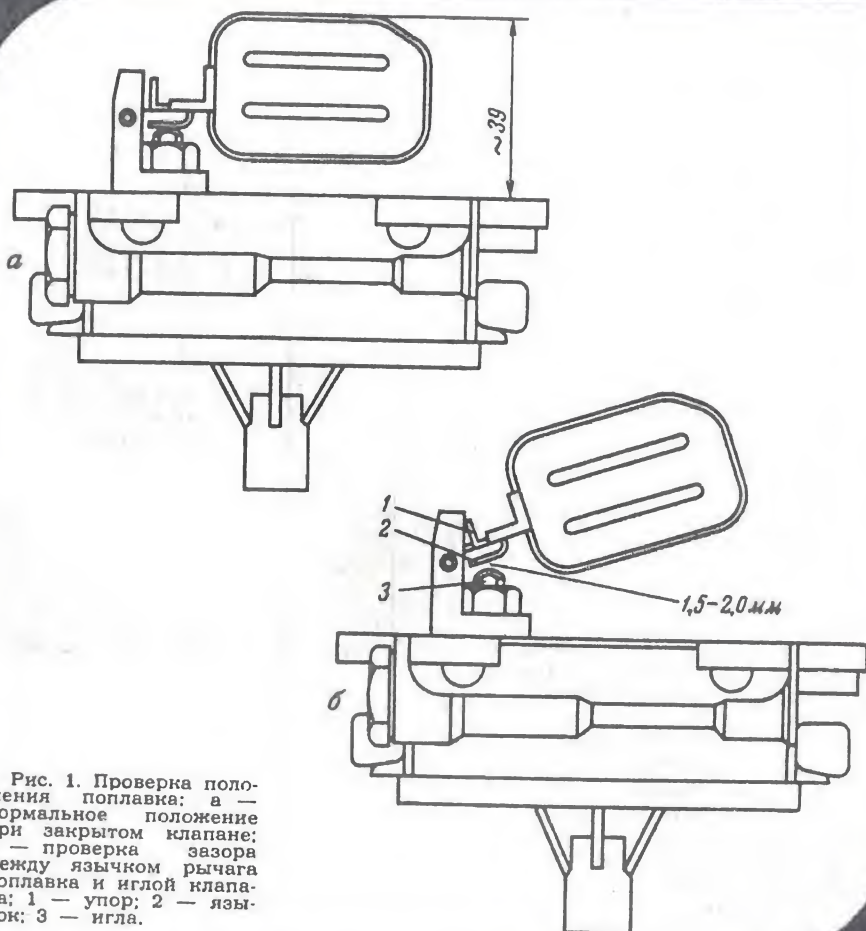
Проверка положения поплавка: а — нормальное положение при закрытом клапане; б — проверка зазора между язычком рычага поплавка и иглой клапана; 1 — упор; 2 — язычок; 3 — игла.
